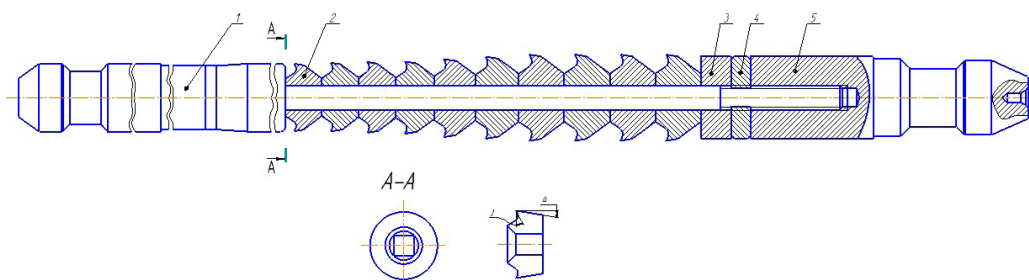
Сборная протяжка с твердосплавными режущими элементами
